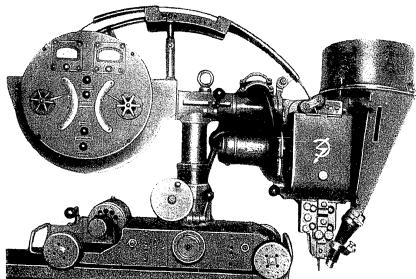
Сварочный трактор двухэлектродного автомата
